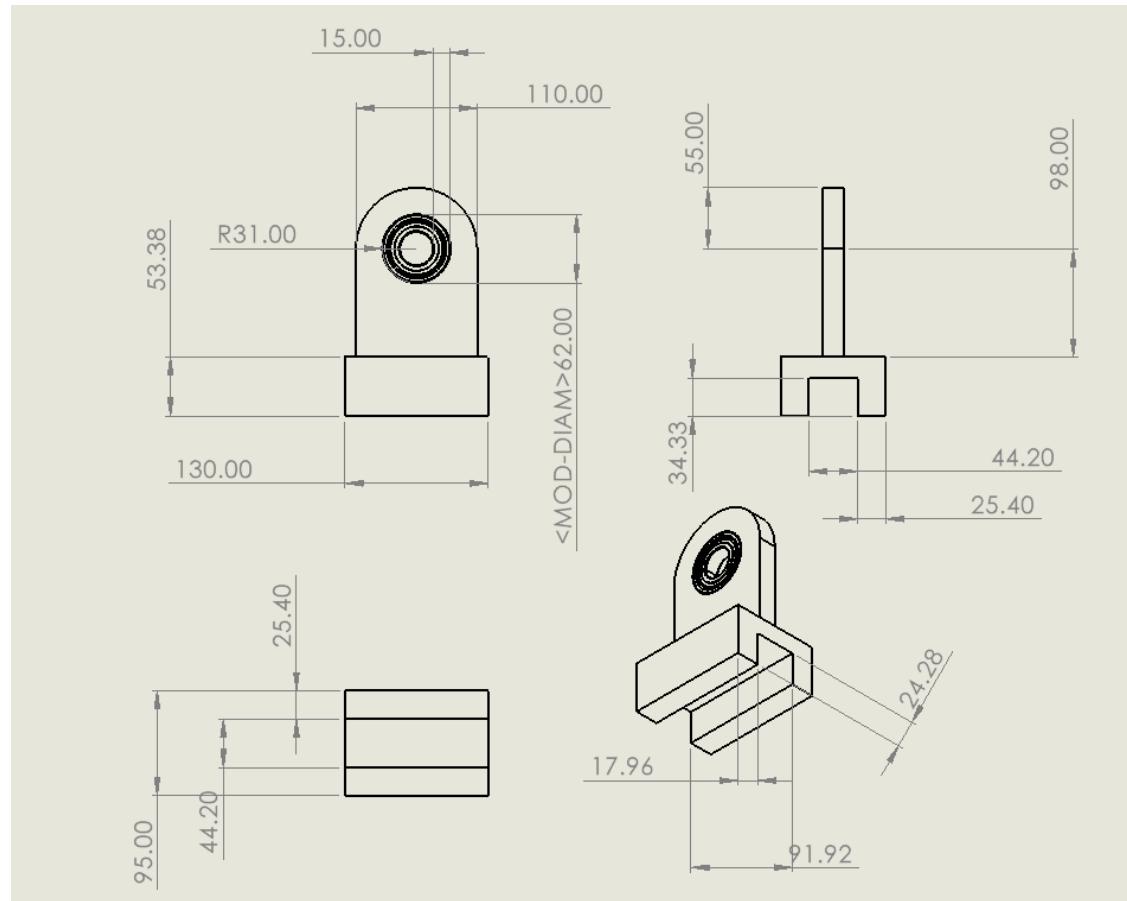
Plano de Soportes embalados con baleros y anclajes
